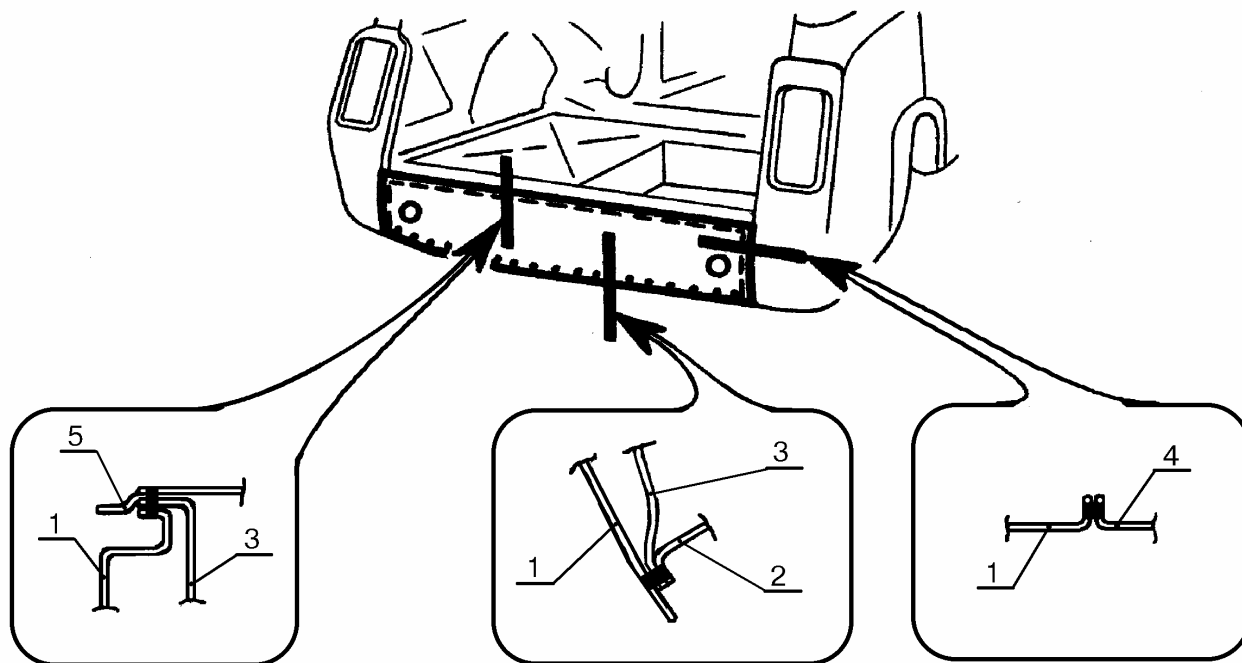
Соединение панели задка наружной с сопрягаемыми деталями.
